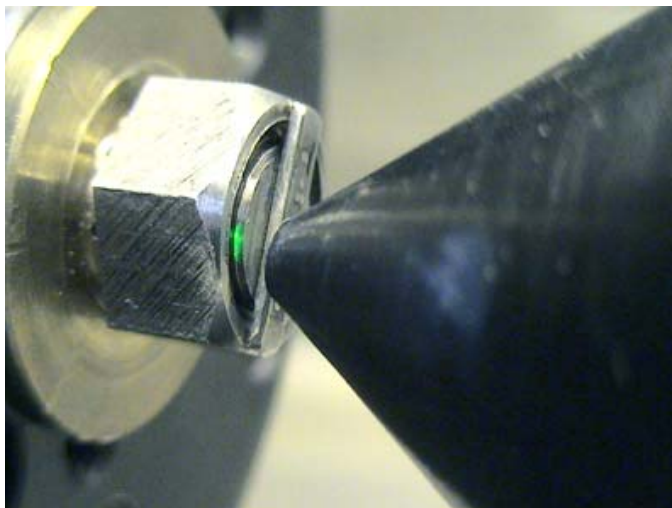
Кондуктор для сборки и выполнения прихваток второго шва в цанге установки СМПЛИ
